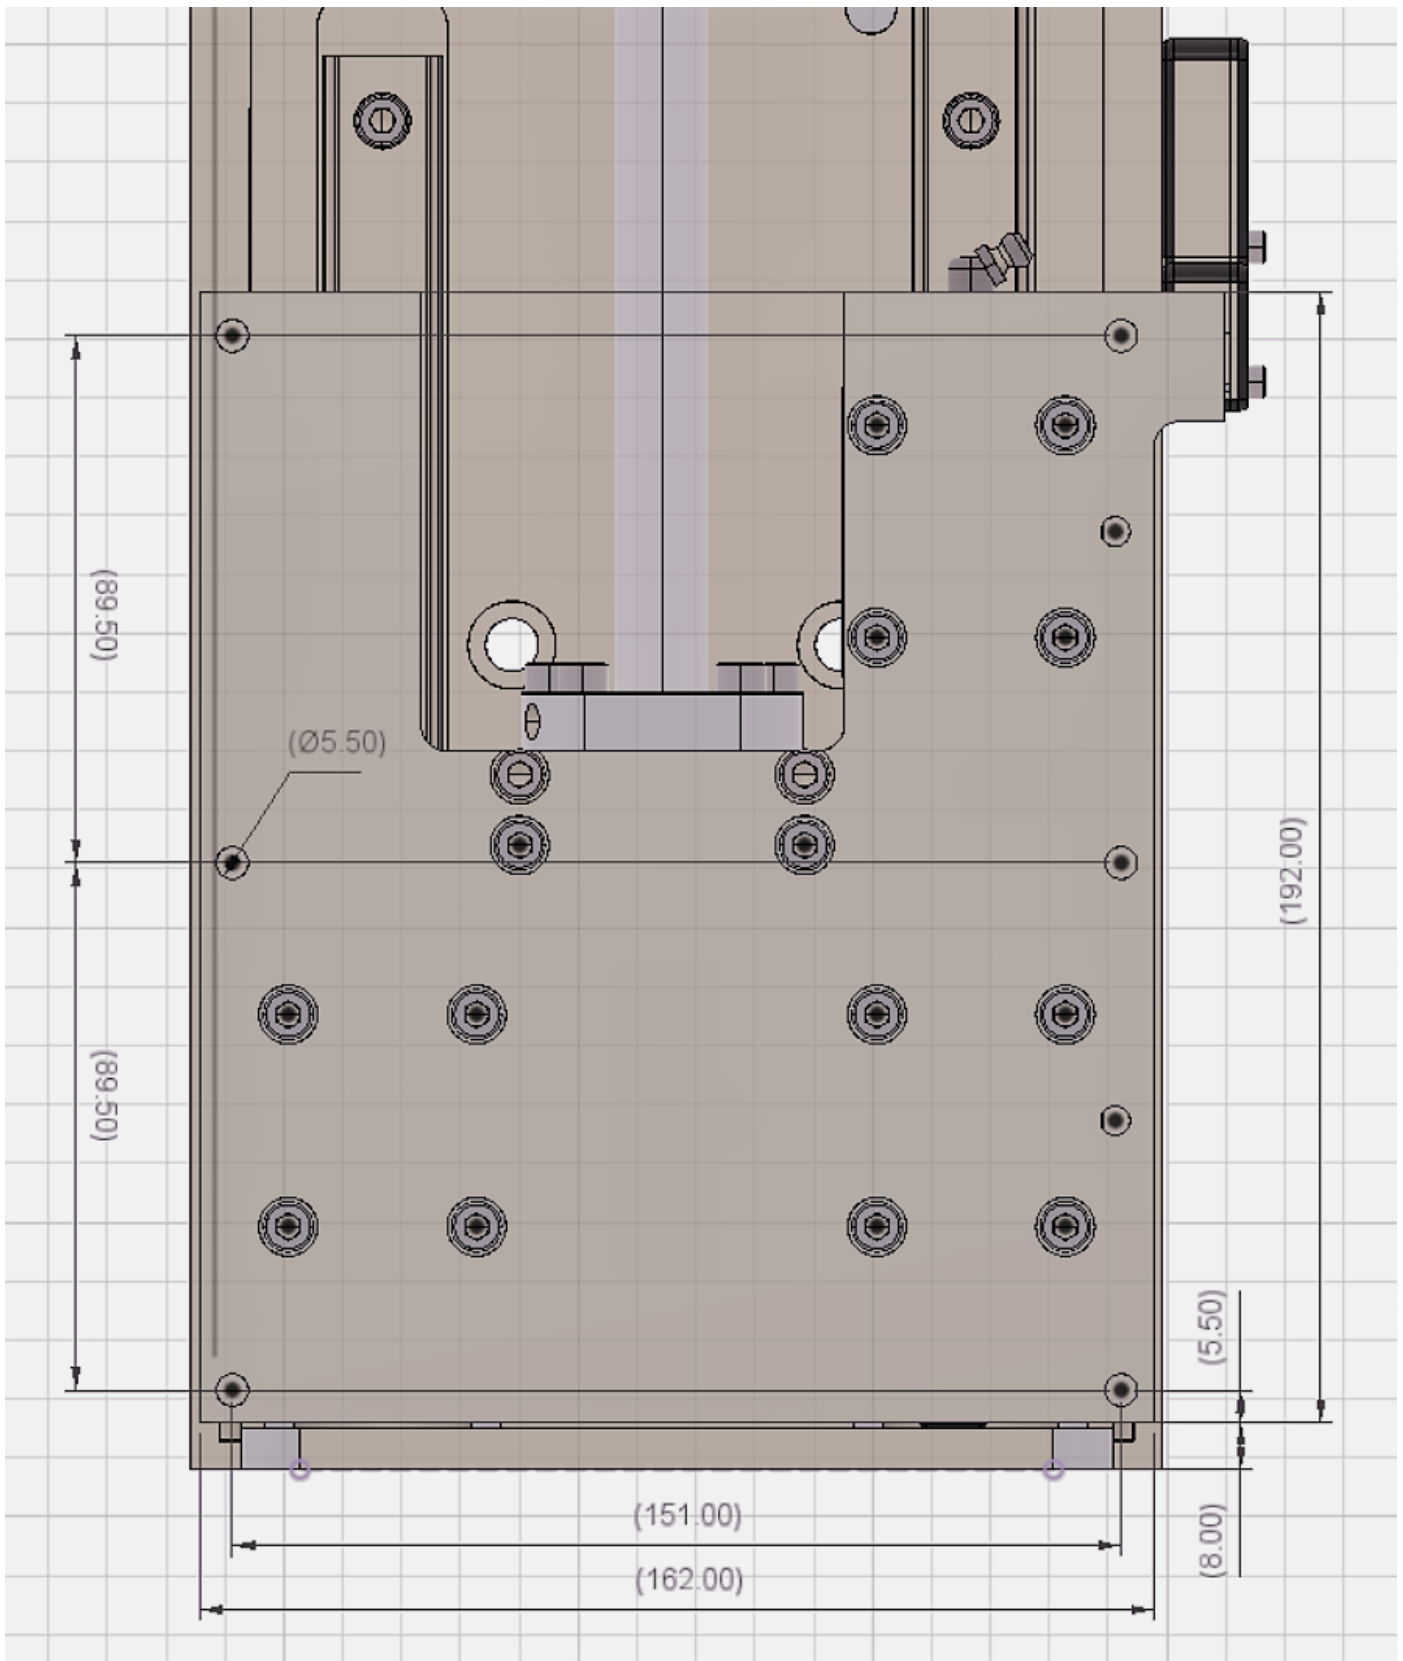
Montagepunkte zur Verschraubung mit dem Portalschlitten
